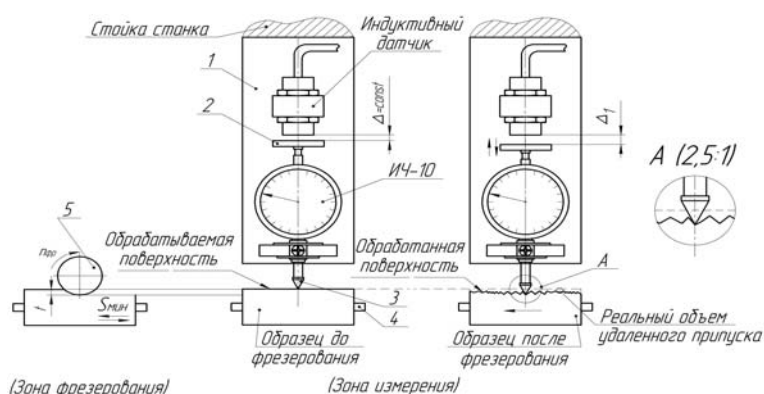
Схема устройства для измерения удаленного припуска и профиля обработанной поверхности:
